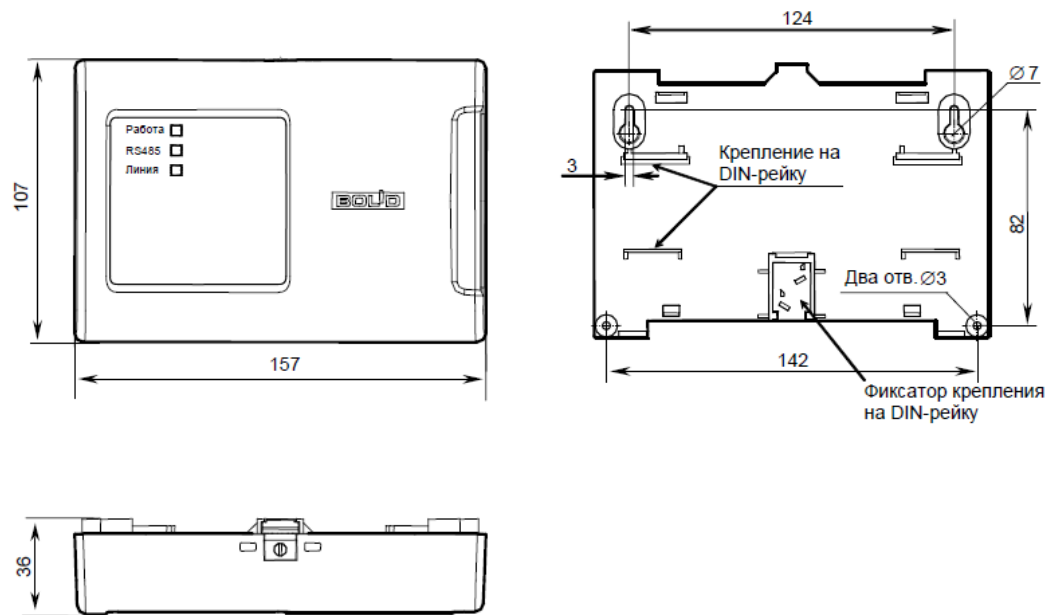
Габаритные и установочные размеры контроллера
